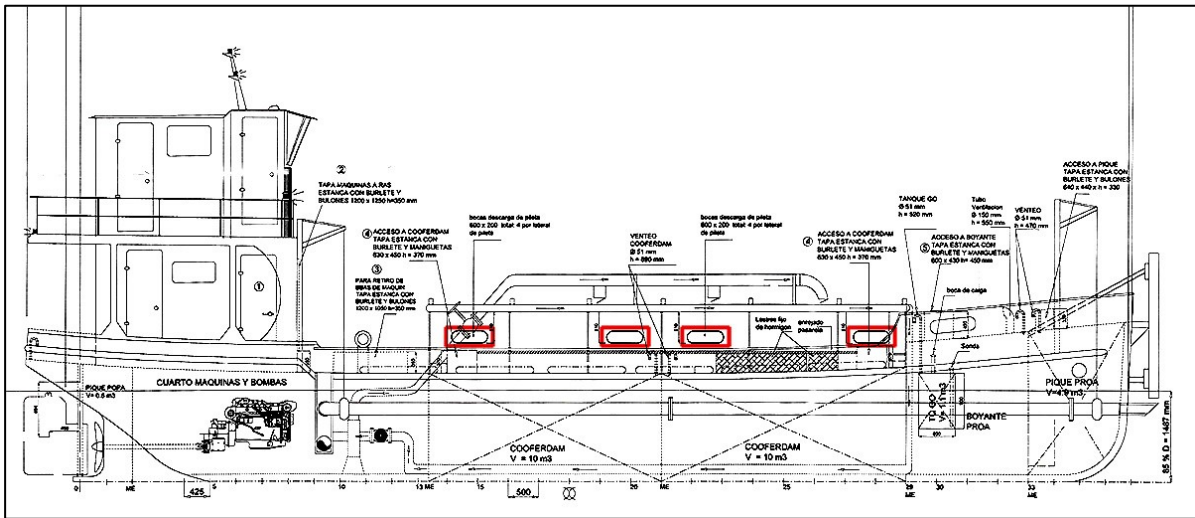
Plano de corte longitudinal donde se observan con color destacado las 4 bocas de descarga de la pileta correspondientes a la banda de estribor
